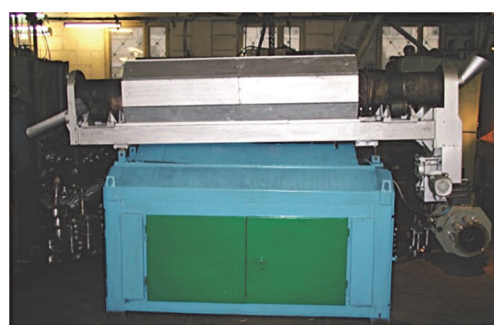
Индукционная установка для нагрева металлической стружки под термоочистку и брикетирование
